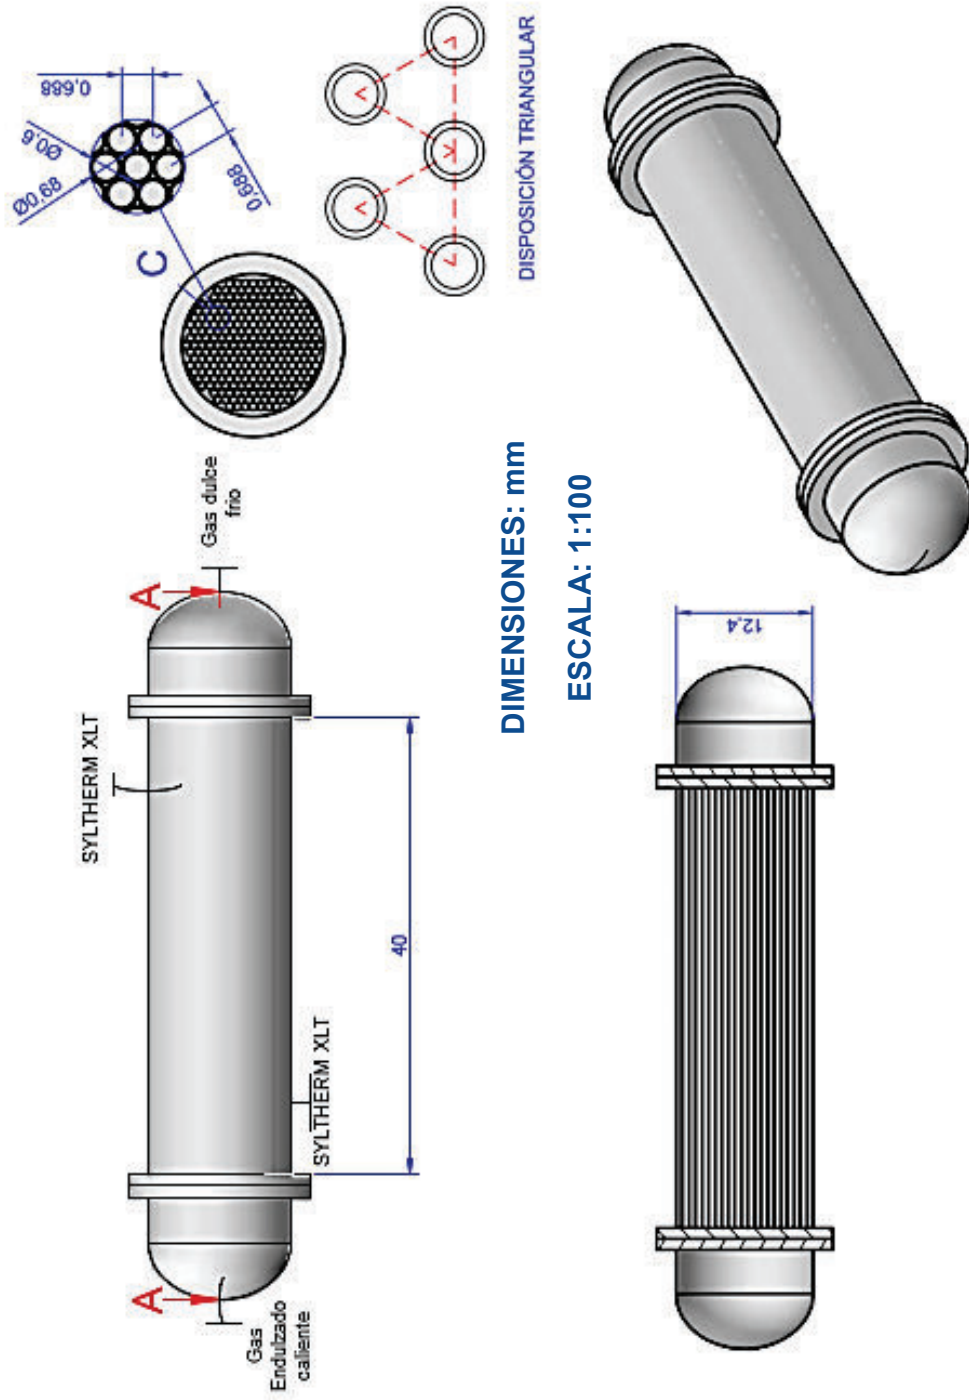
Dimensiones del intercambiador de calor 1 de tubos y coraza (E-401)
